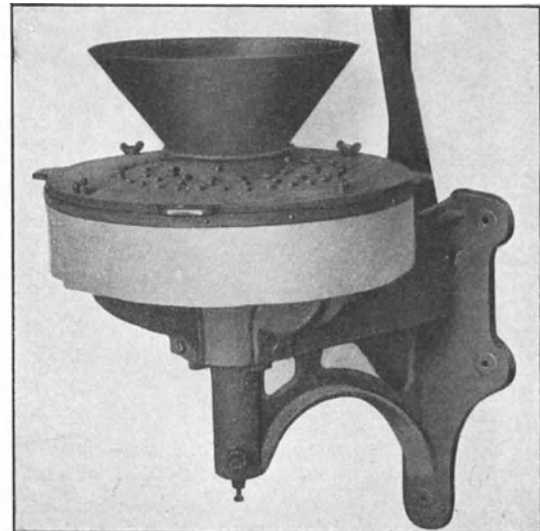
An der Wand befestigte stehende Sandschleudermaschine.
